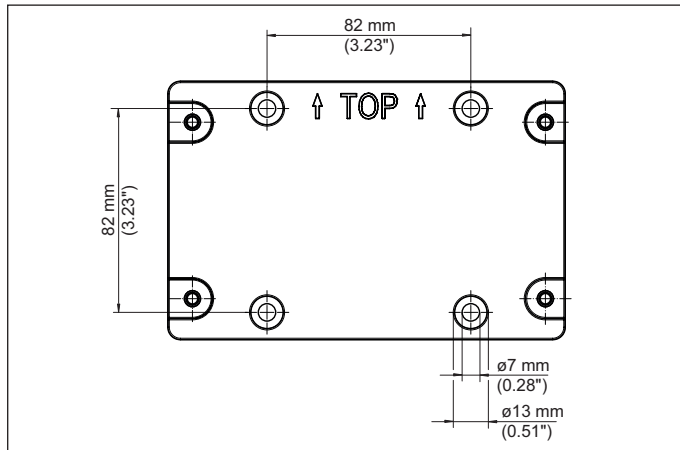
Montageplaat voor wandmontage (VEGAMET 841, 842)
